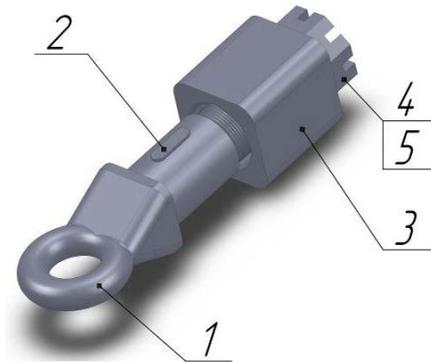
Установка шпонки для стопорения петли сцепной поворотной:
